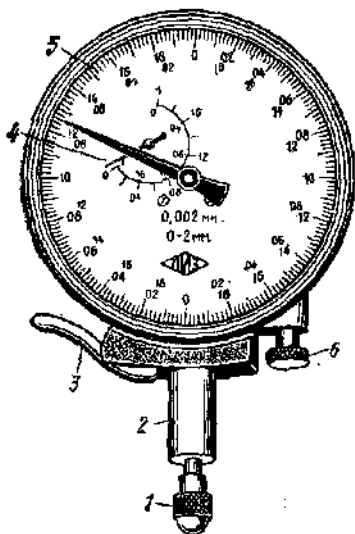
Многооборотная рычажно-зубчатая измерительная головка типа МИГ:
